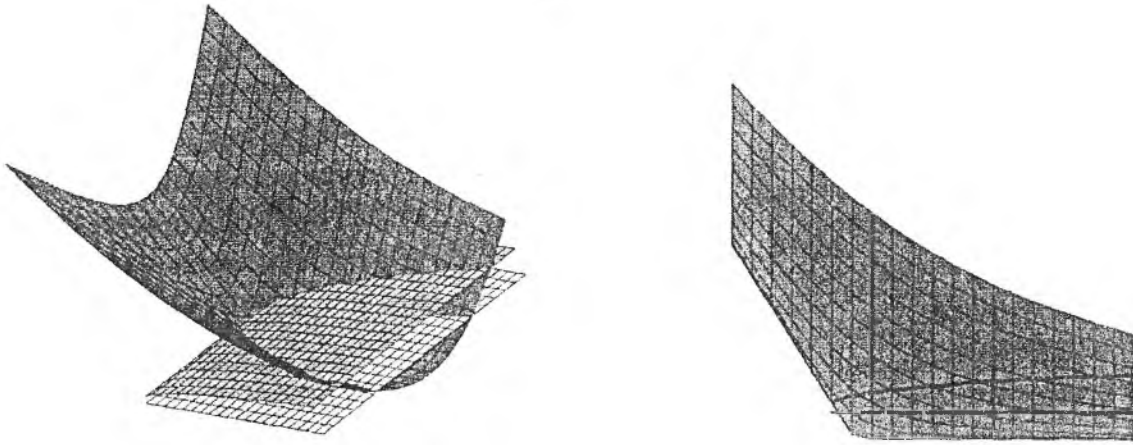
Взаємне розташування поверхонь інструменту, нездеформованої заготовки та найвищого положення гребінця хвилі
